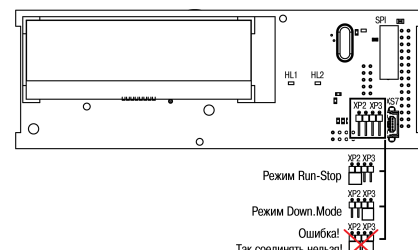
Вид на верхнюю плату со снятой крышкой
